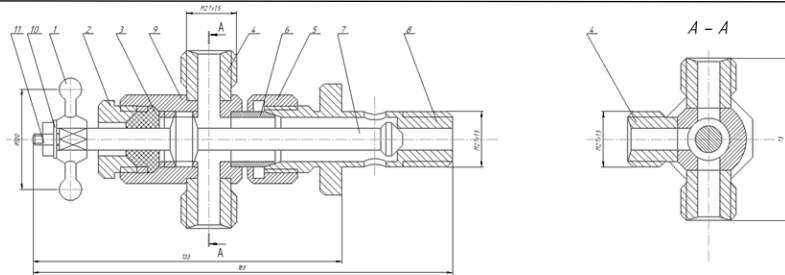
Приспособление для включения агрегатов гидросистемы
